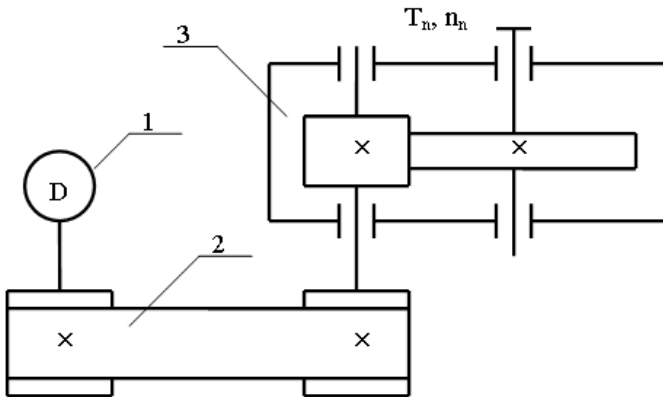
Схема механічного приводу в складі: 1 – електродвигун; 2 – зубчасто-пасова передача; 3 – редуктор циліндричний
